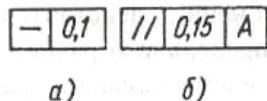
Обозначение допусков формы и расположения поверхностей
